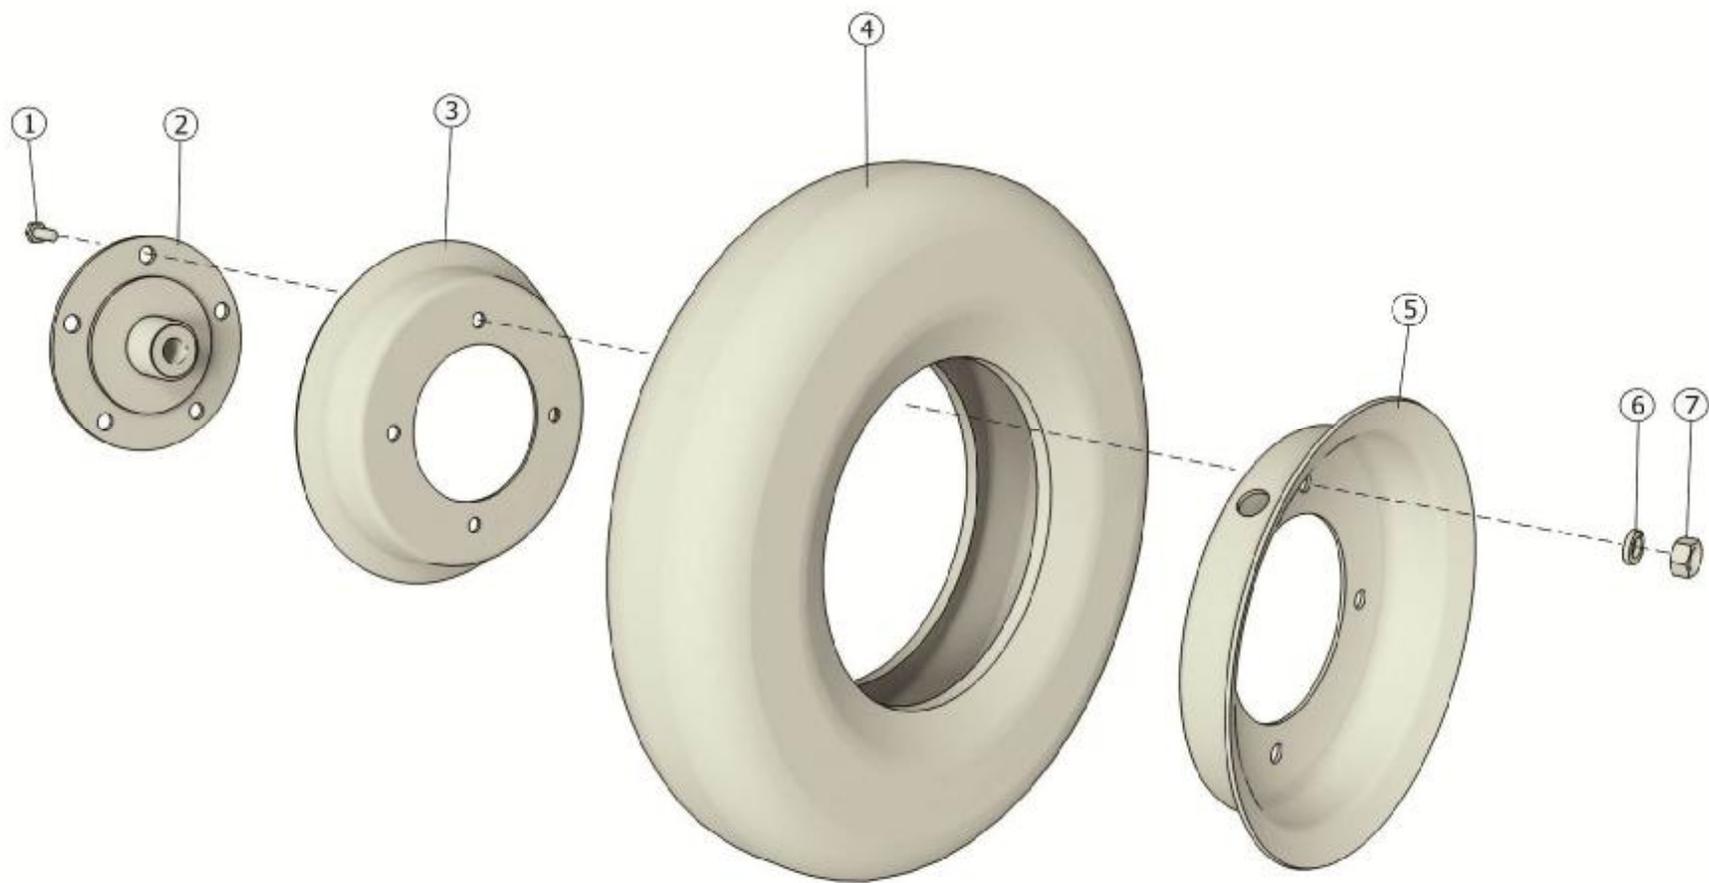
Колесо в сборе МЗС-90.01.100
